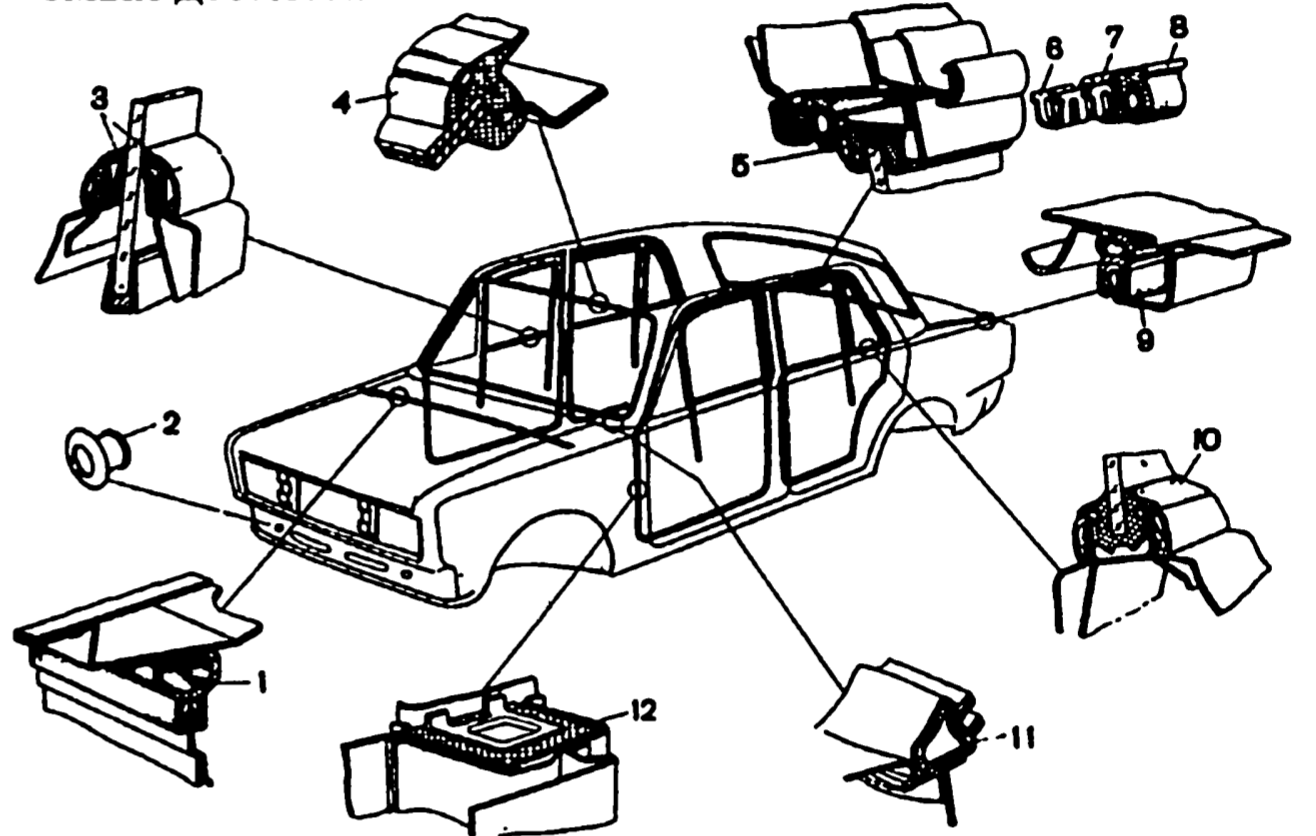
Резиновые уплотнители: 1 - капота; 2 - соединителя бампера; 3 - нижнего уплотнителя стекла двери; 4 - ветрового и заднего стекол; 5 - опускного стекла; 6 - каркаса уплотнителя; 7 - канта уплотнителя; 8 - проема двери; 9 - крышки багажника; 10 - неподвижного стекла двери; 11 - рамы ветрового окна; 12 - передней стойки
